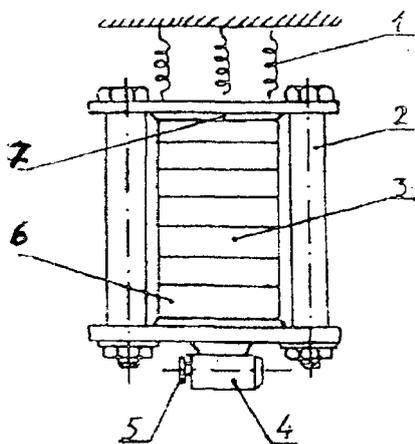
Схема вибровстряхивателя: 1 - пружинная подвеска; 2 – стягивающие болты; 3 – набор стандартных сит; 4 - электродвигатель; 5 - эксцентрик; 6 - поддон; 7 -крышка
